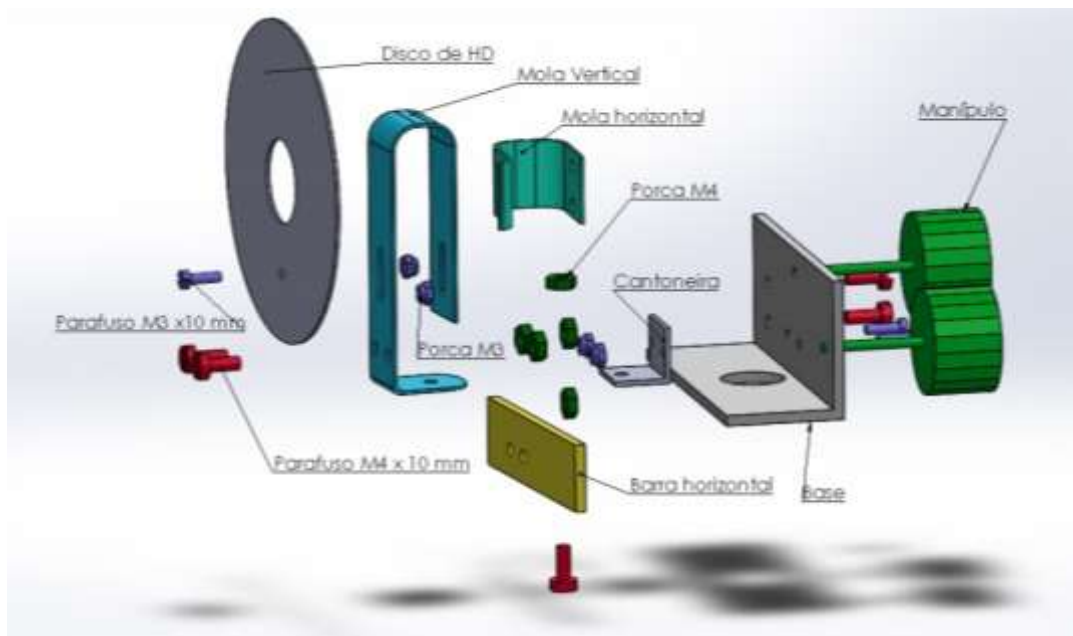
Suporte do espelho de Hd. Vista explodida com descrição.
